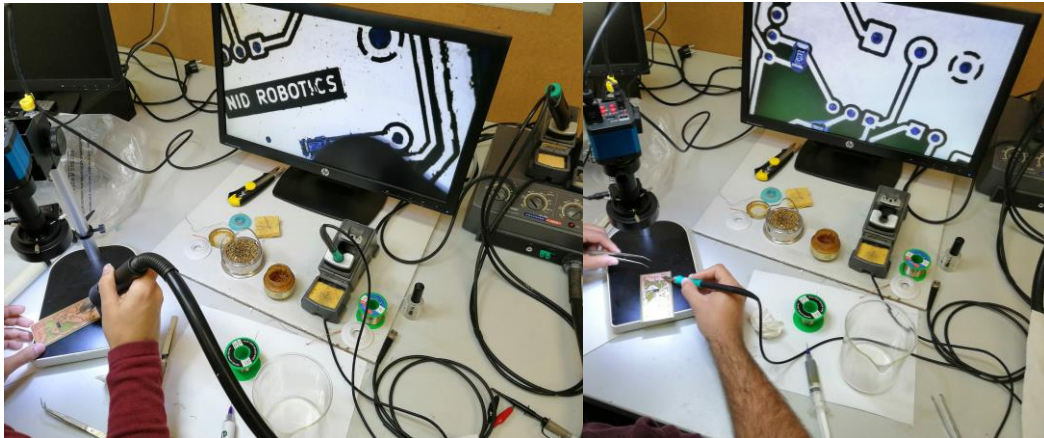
A la izquierda corrección de soldaduras SMD con pistola de calor a la derecha con soldador
